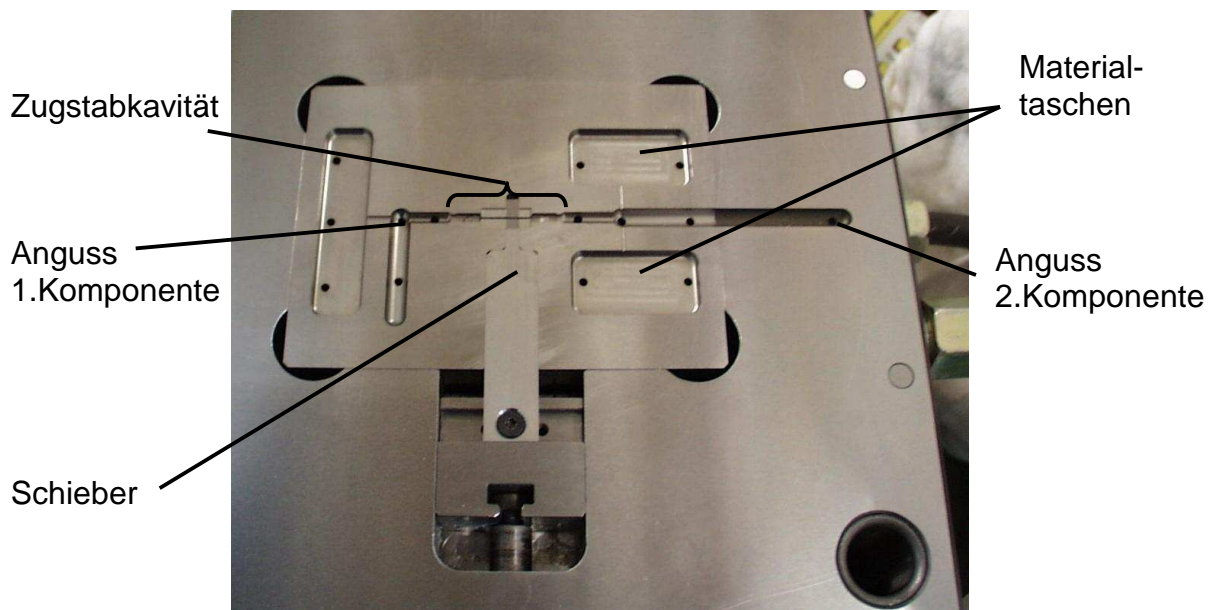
2K-PIM-Werkzeug mit Formeinsatz Zugstab (Auswerferseite)
